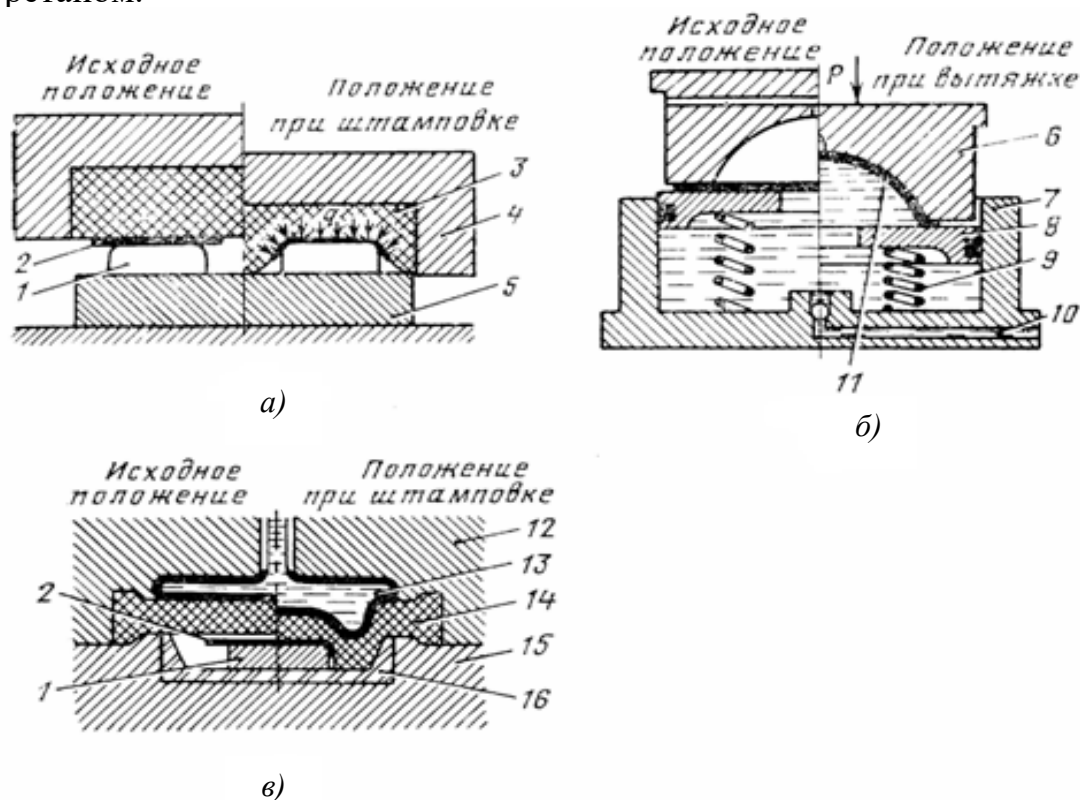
Схемы штамповки: а – резиной (полиуретаном);
